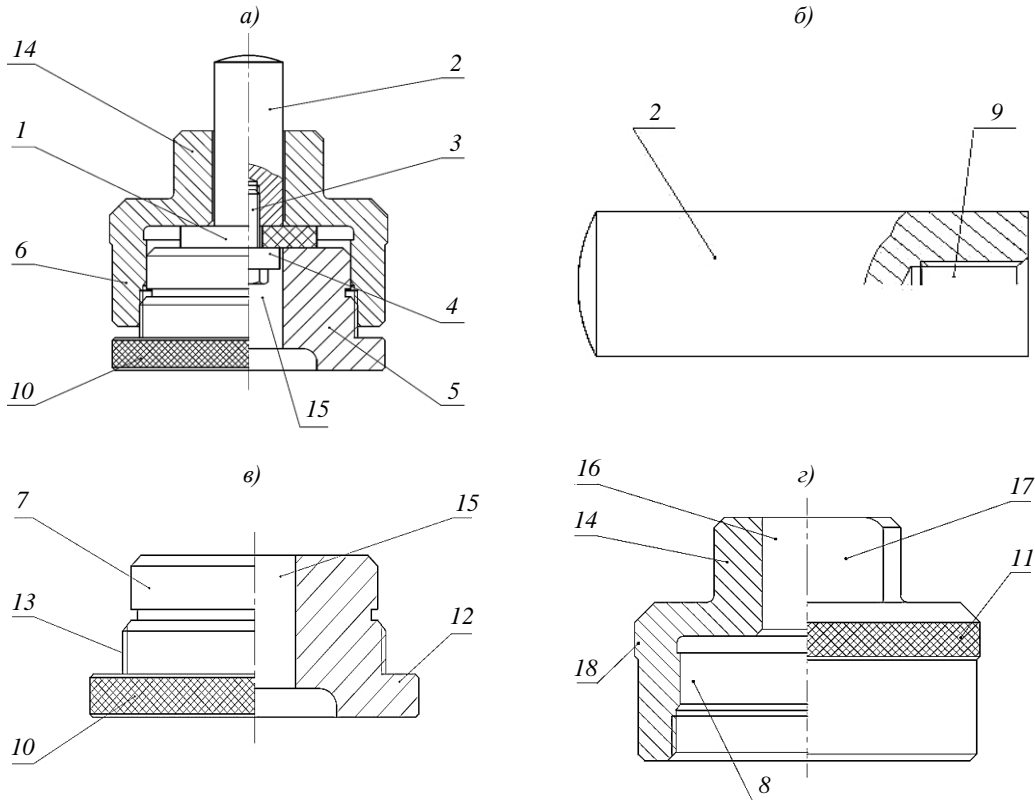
Конструкция приспособления для испытания пластин на срез: устройство в сборе (а); срезающий пуансон (б); матрица (в); прижим (г); элементы: 1 – образец для испытания; 2 – срезающий пуансон; 3 – болт; 4 – шайба; 5 – матрица; 6 – прижим; 7 – центрирующий поясok матрицы; 8 – центрирующий поясok прижима; 9 – отверстие с резьбой для болта; 10 – рифление на внешней поверхности матрицы; 11 – рифление на внешней поверхности прижима; 12 – буртик с рифлением на матрице; 13 – резьба; 14 – выступ в верхней части прижима; 15 – центральное отверстие матрицы; 16 – центральное отверстие прижима; 17 – лыски под ключ; 18 – буртик с рифлением на прижиме [13]
